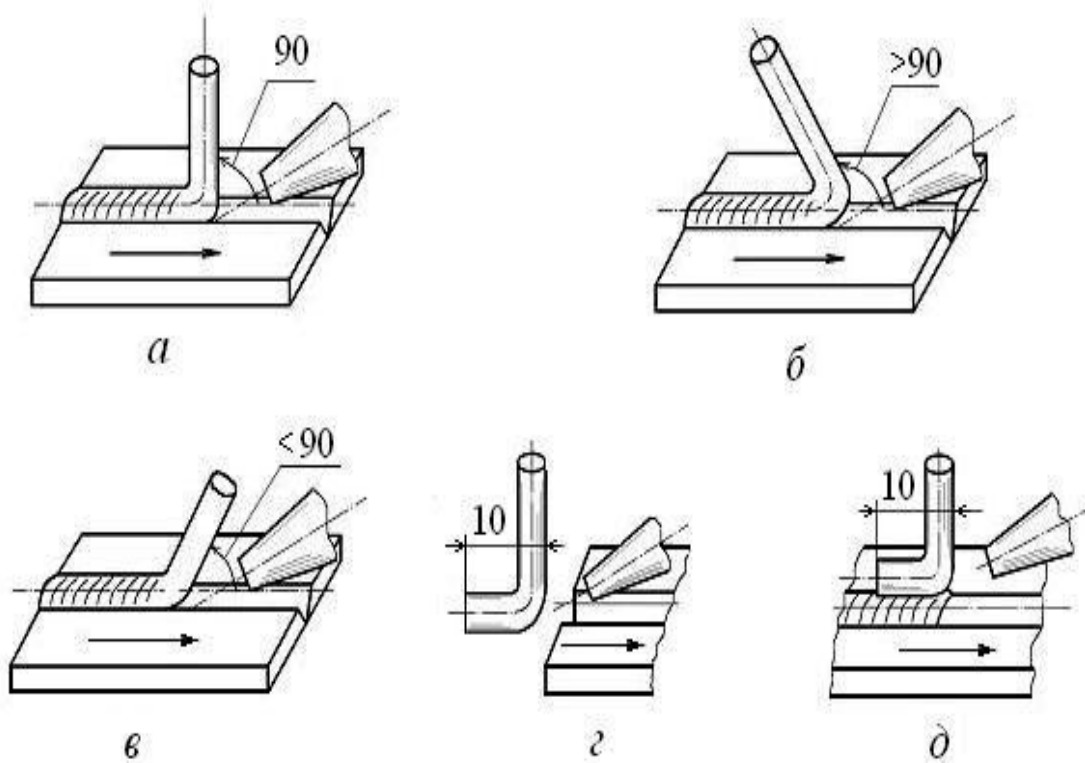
Положення присадного прутка та пальника при зварюванні.
